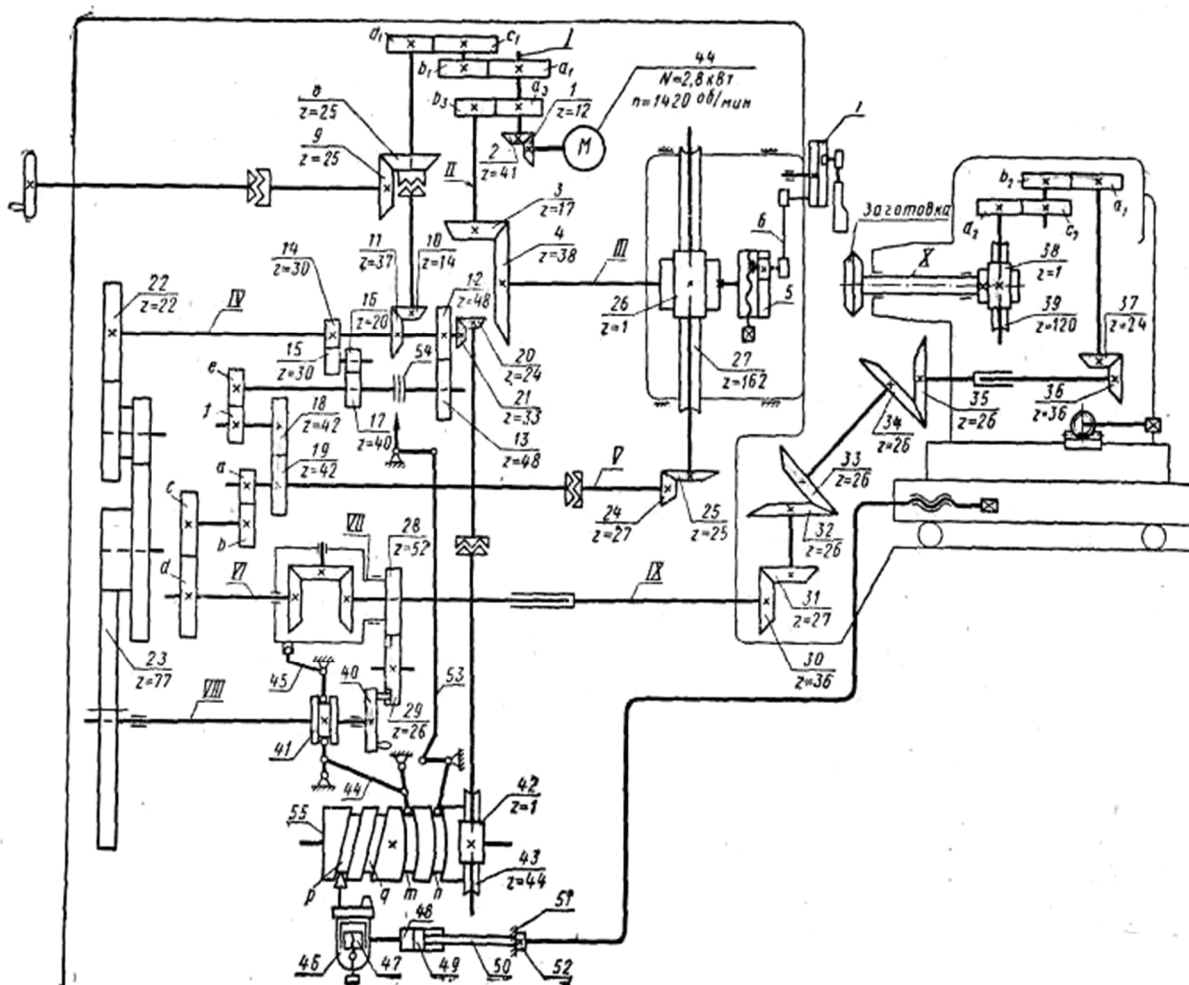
Кинематическая схема зубострогального станка для обработки прямозубых конических колес модели 5А26
